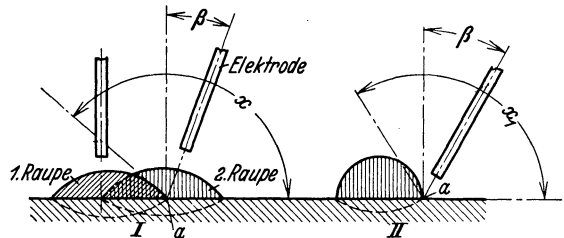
Elektrodenhaltung quer zur Schweißrichtung.
